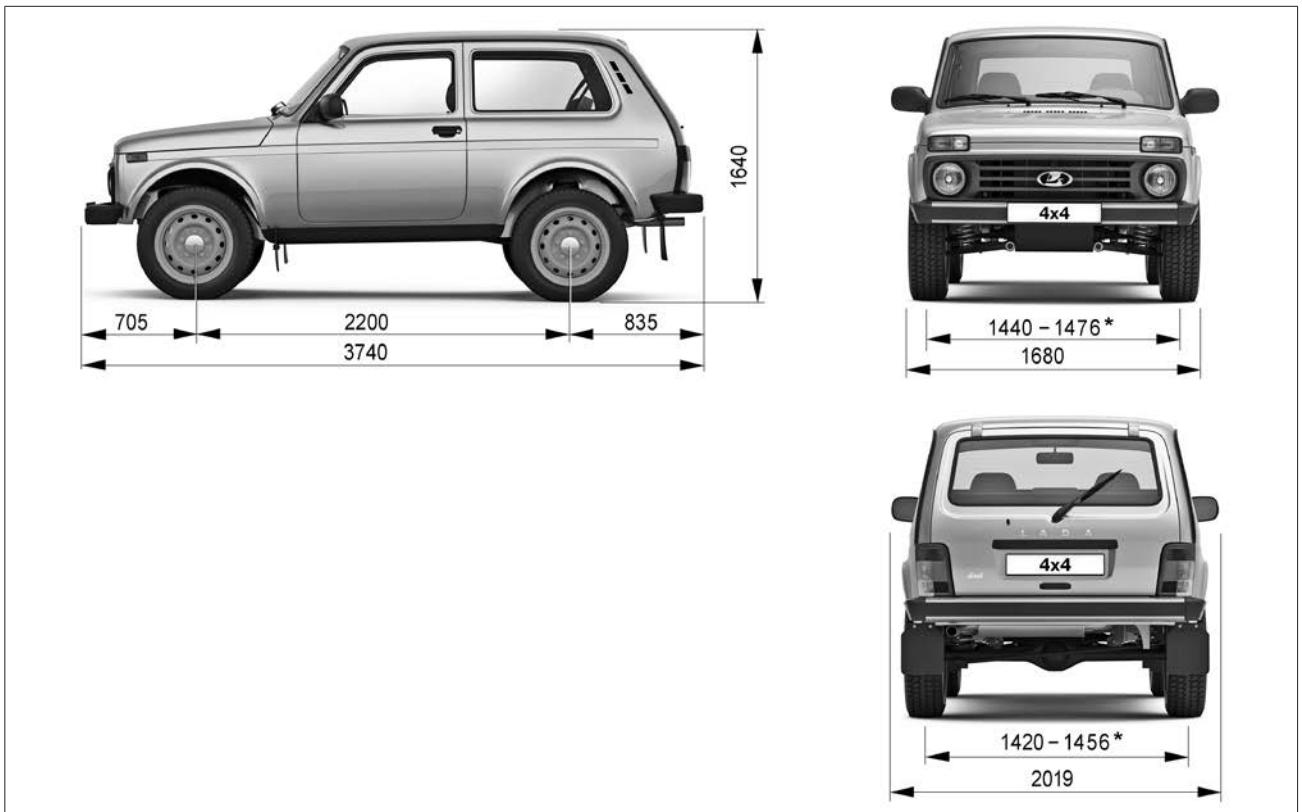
Габаритные размеры автомобиля LADA 4x4 3 дв.
